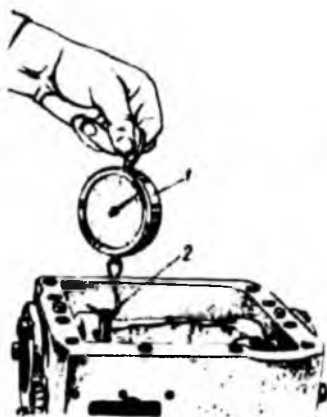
Проверка усилия затяжки подшипников цапф люльки:
